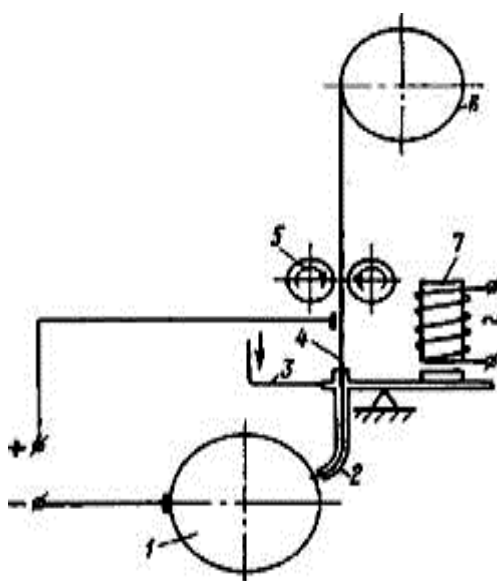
Схема установки для вібродугового наплавлення
